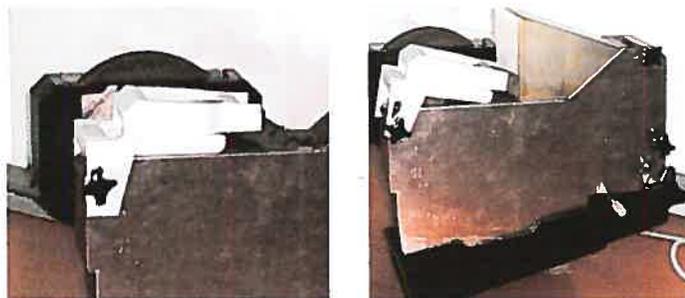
Prototype sur la machine à l'UQAM¹⁴⁶
